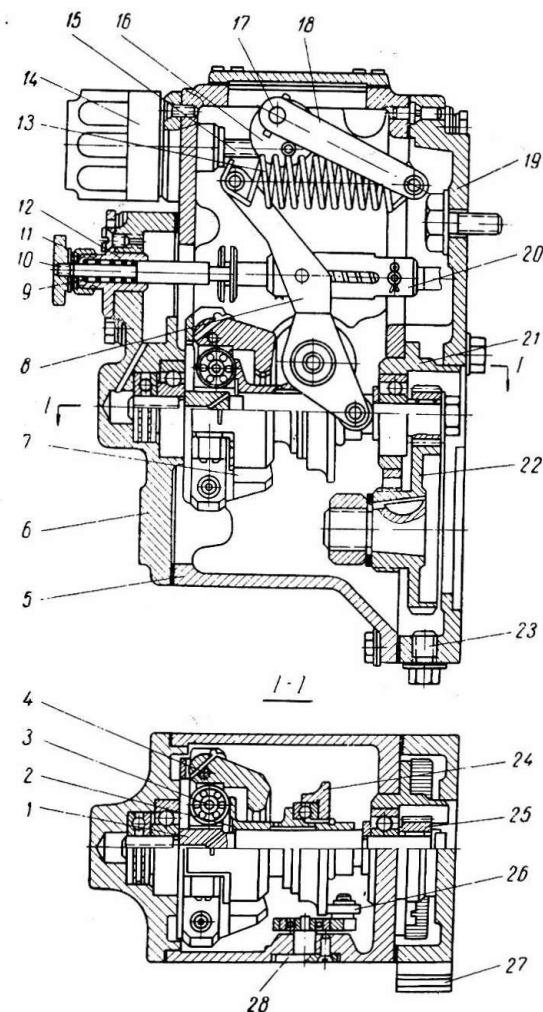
Центробежный однорежимный регулятор дизелей 4ч-6ч:
